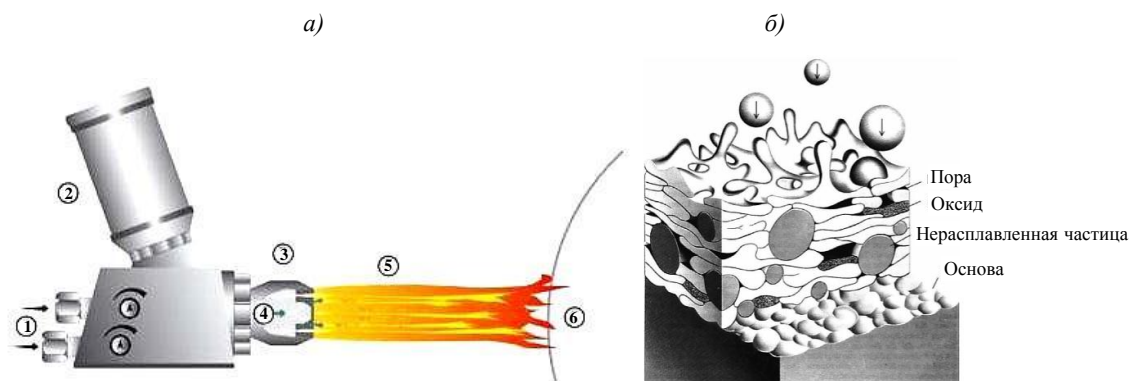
Принципиальная схема газопламенного напыления порошком (а: 1 – кислород/ацетилен; 2 – контейнер с порошком; 3 – горелка; 4 – порошок + газ; 5 – ацетилен-кислородное пламя и напыляемые частицы; 6 – деталь) и схема формирования напыленного покрытия (б)
